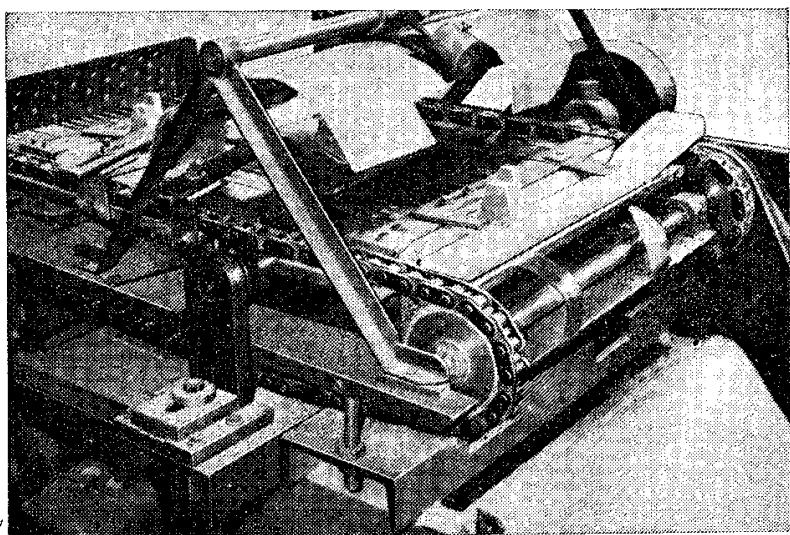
Мензурный станок с механической подачей для пропиливания пазов в наклейке под ладовые пластины
